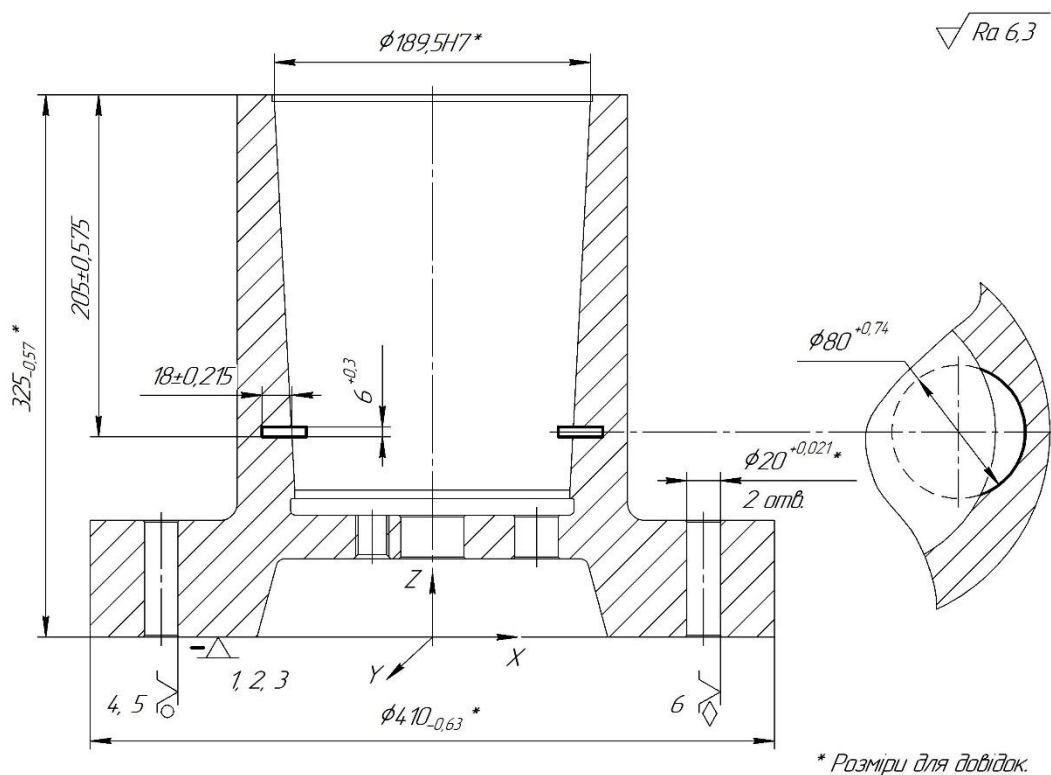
Схема базування заготовки на фрезерній з ЧПК операції 110
